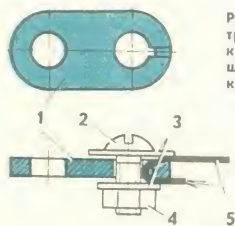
Крепление троса: 1 — планка; 2 — винт; 3 — шайбы; 4 — гайка; 5 — трос.
